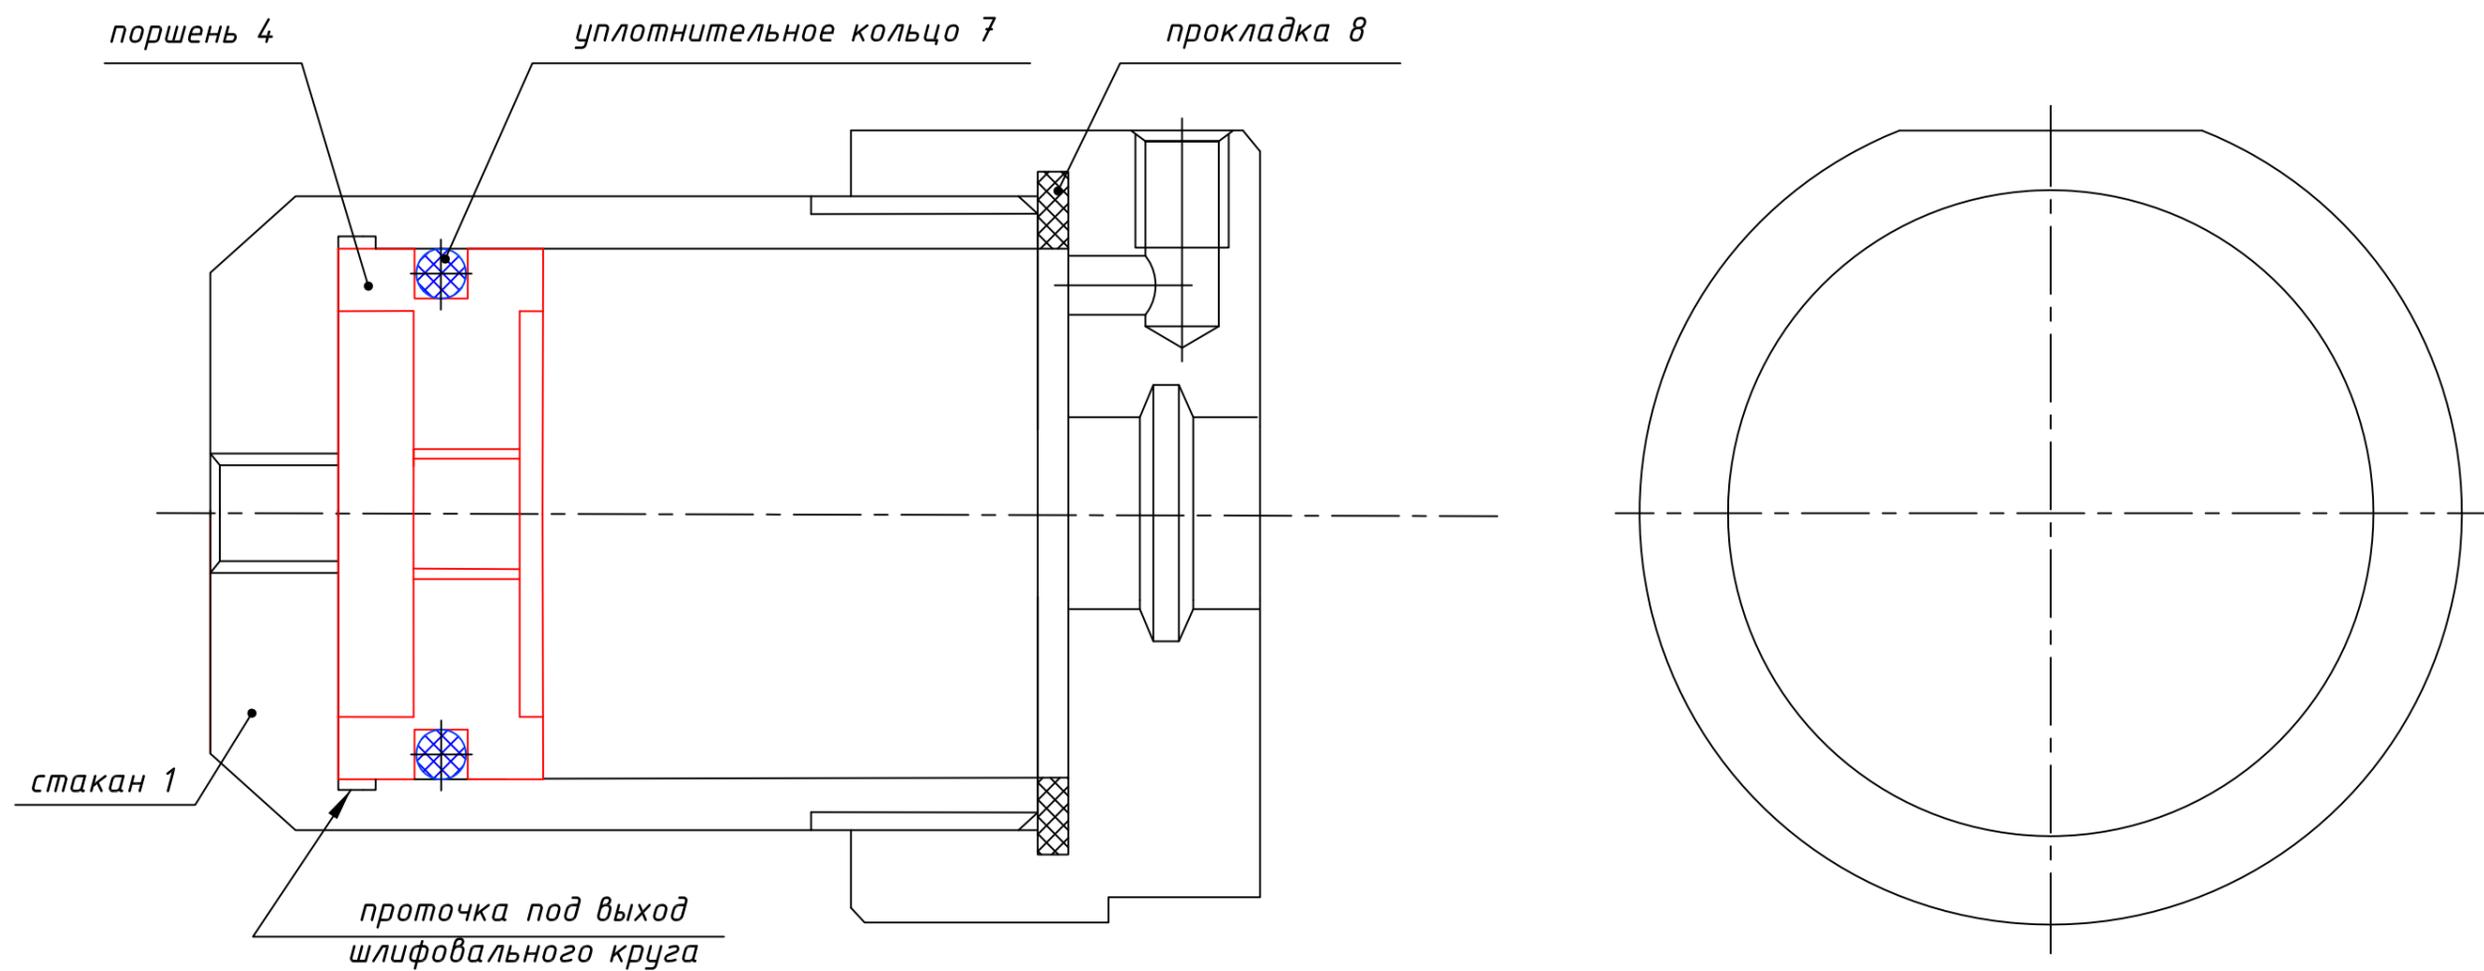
Установка в стакан 1 поршня 4 и уплотнительного кольца 7
